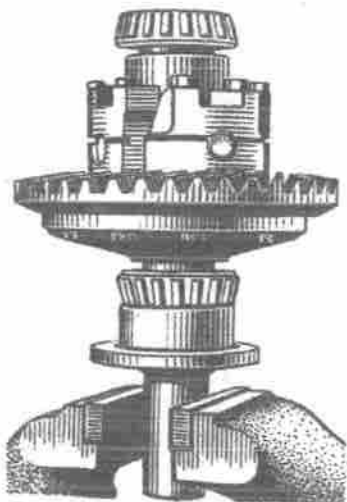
Vorläufiges Aufpressen der inneren Laufringe der Ausgleichgetriebeleger
